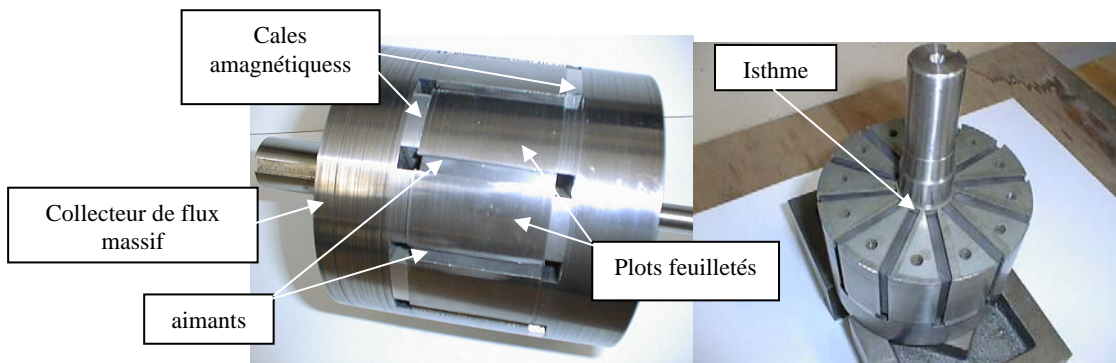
Photo du rotor de la machine M4 en configuration bipolaire (stator identique à celui de M3)
